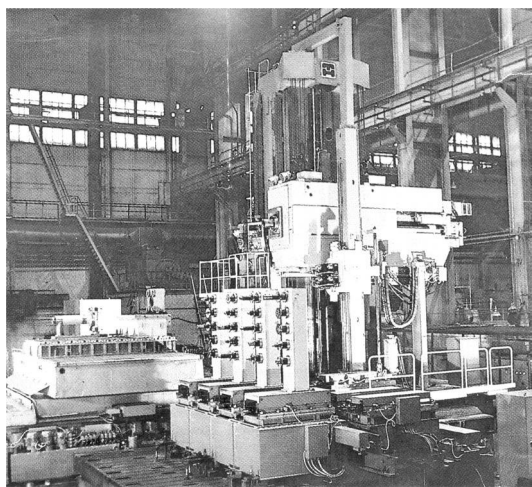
Тяжелый многоцелевой станок сверлильно-фрезерно-расточной группы с поворотно-подвижным столом для обработки корпусных деталей массой до 200 т
